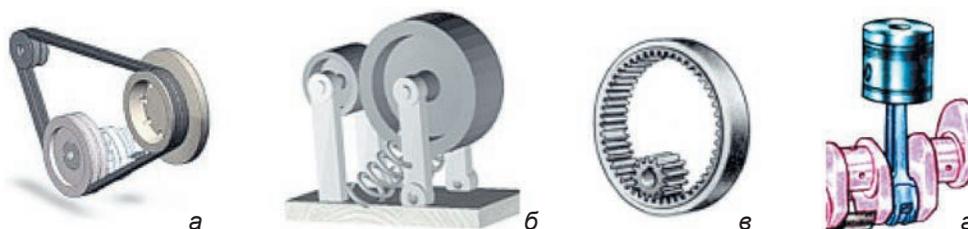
Механизмы передачи движения: а – пас; б – фрикционный; в – зубчатый; г – кривошипно-шатунный
